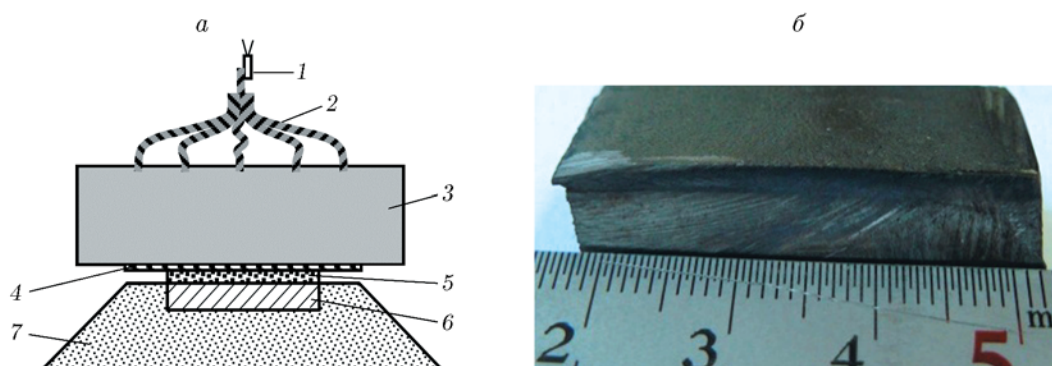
Схема нагружения (а) и внешний вид полученных образцов (б):
